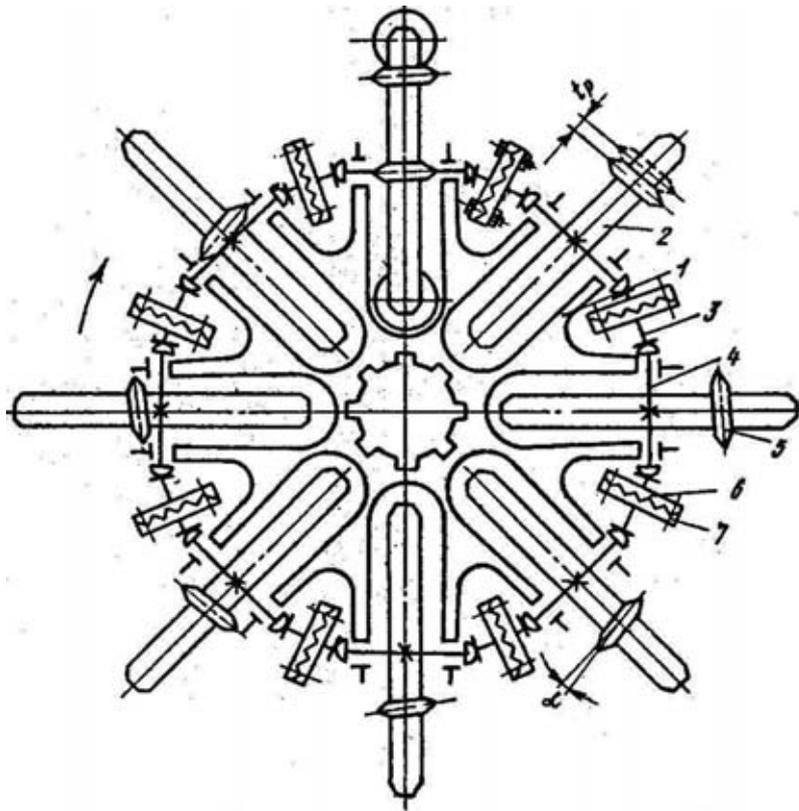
Кинематическая схема роторно-планетарного рабочего органа
